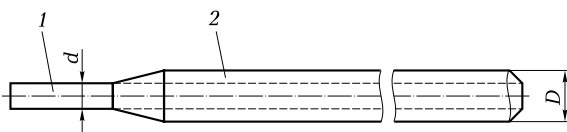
Схема покрытого электрода для ручной дуговой сварки:
